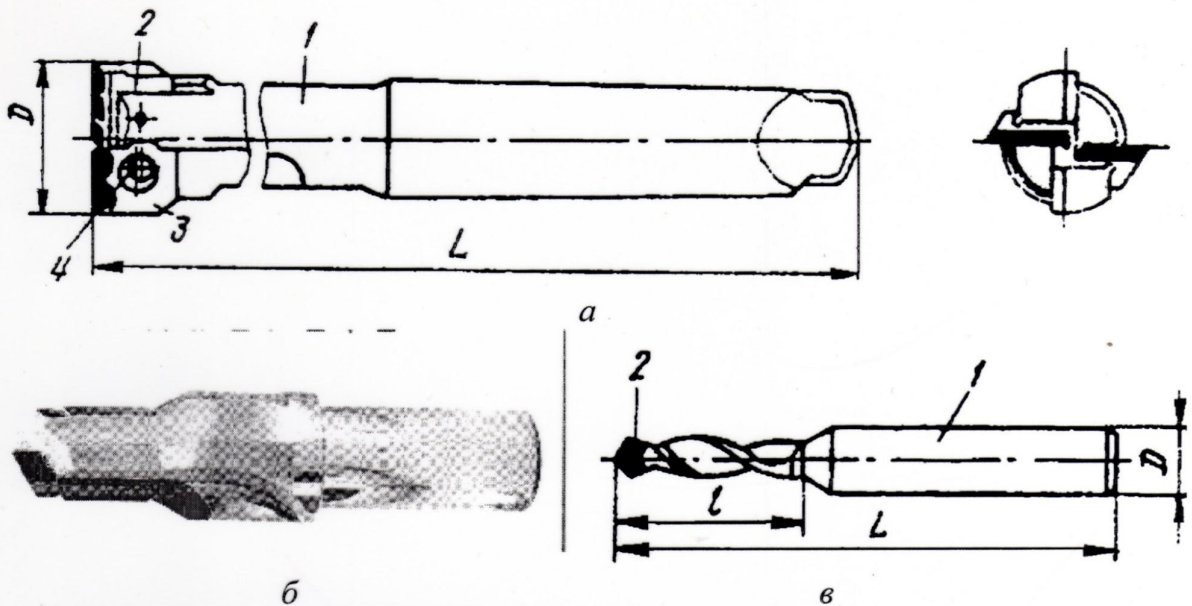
Сверла, оснащенные ПСТМ, с механическим креплением режущих элементов (а); с прямыми (б) и спиральными (в) канавками и паяными режущими элементами: 1 – корпус; 2, 3 – сменные ножи (устанавливают в сверла и крепят винтами 4 к корпусу через фасонные отверстия).
